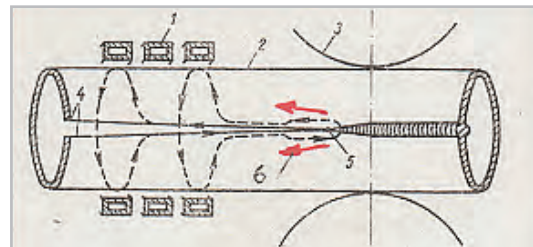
Схема индукционного метода высокочастотной сварки труб
